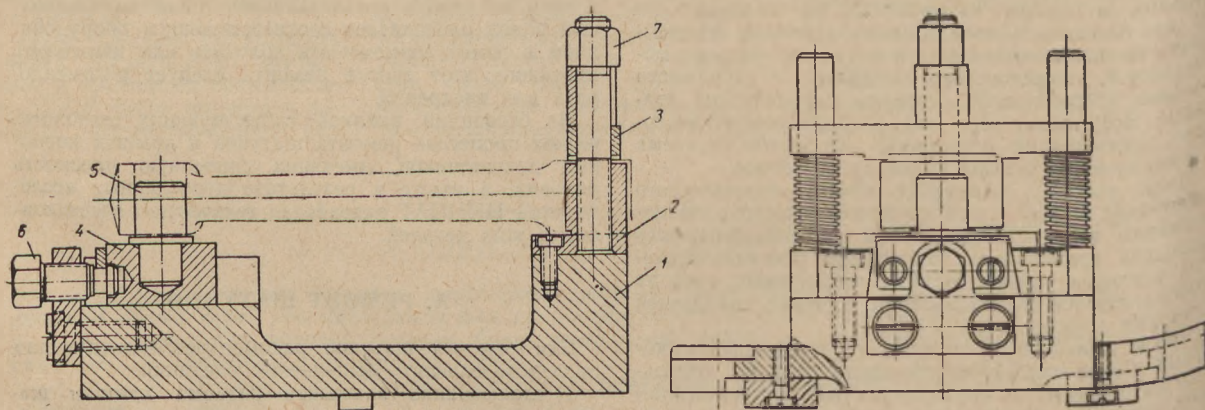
Приспособление для фрезерования плоскости разъема шатунов двигателей ГАЗ-51:
